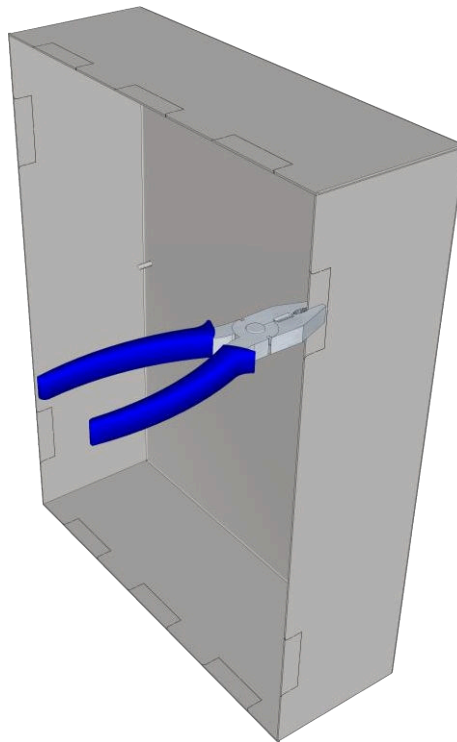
Metodo di rottura della sporgenza per i cavi di installazione.
